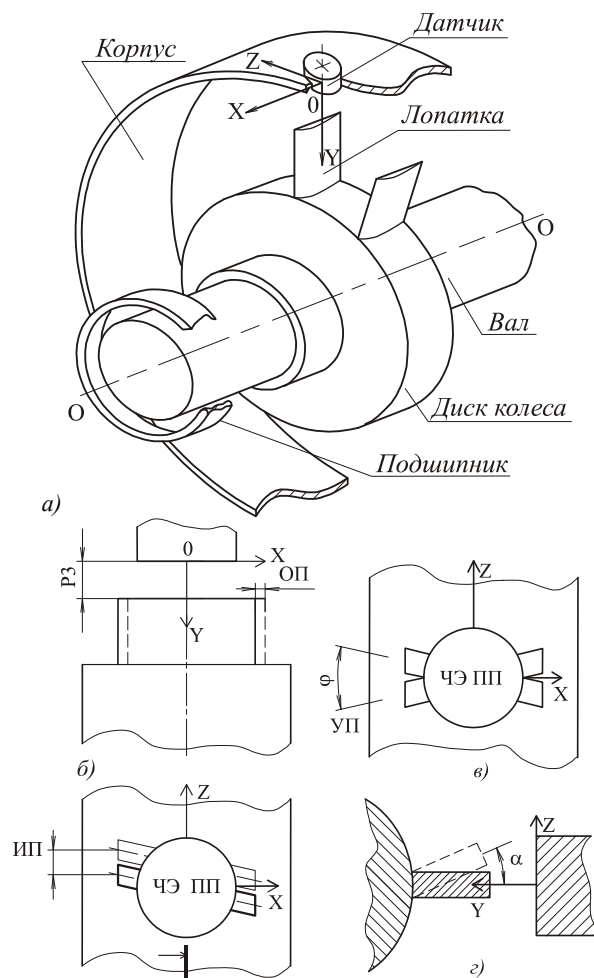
Элементы ротора лопаточной энергетической установки (а) и развёртка лопаточного венца с линейными (б) и угловыми (в, г) перемещениями лопаток
